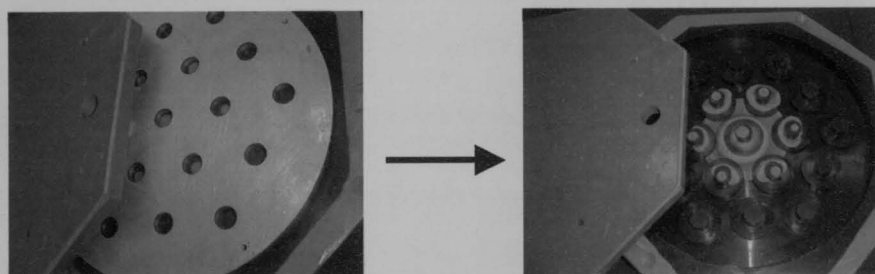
21 - Ilustração da ferramenta de revestimento de silicone para a placa de molde.
